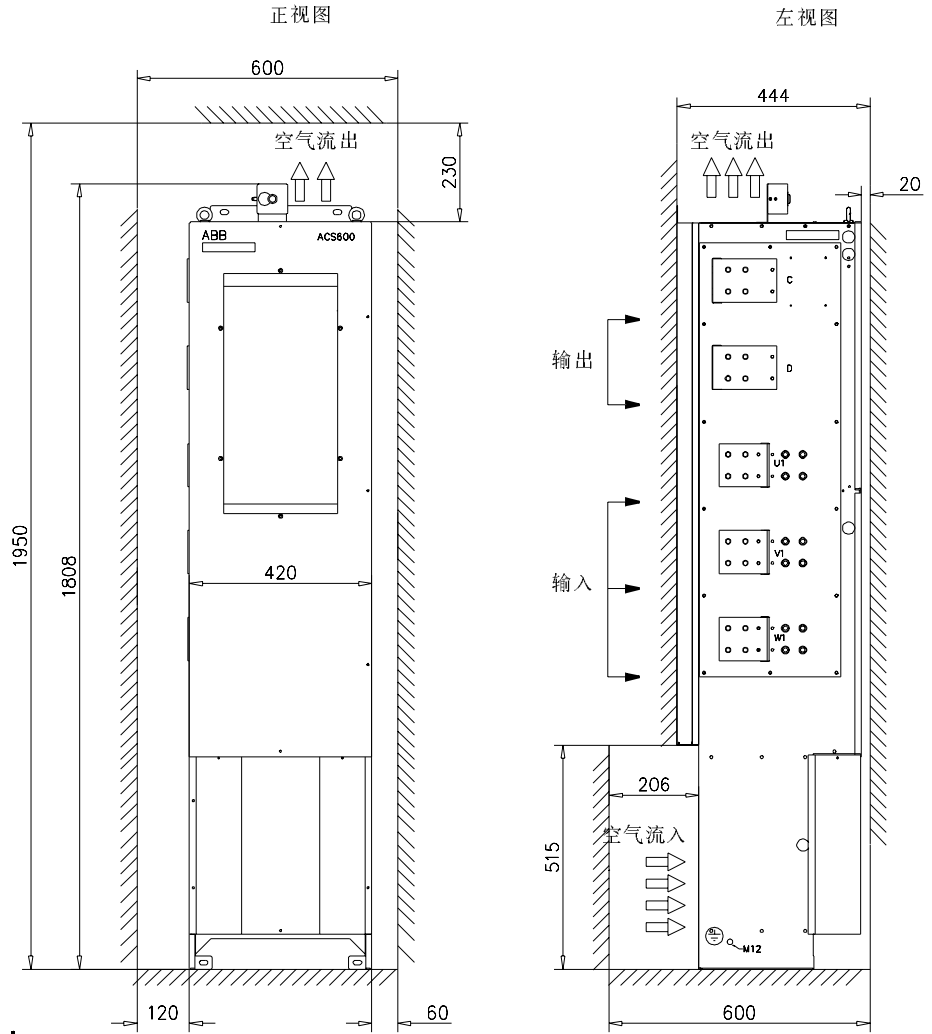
外形尺寸 B5 供电模块的尺寸和间距
